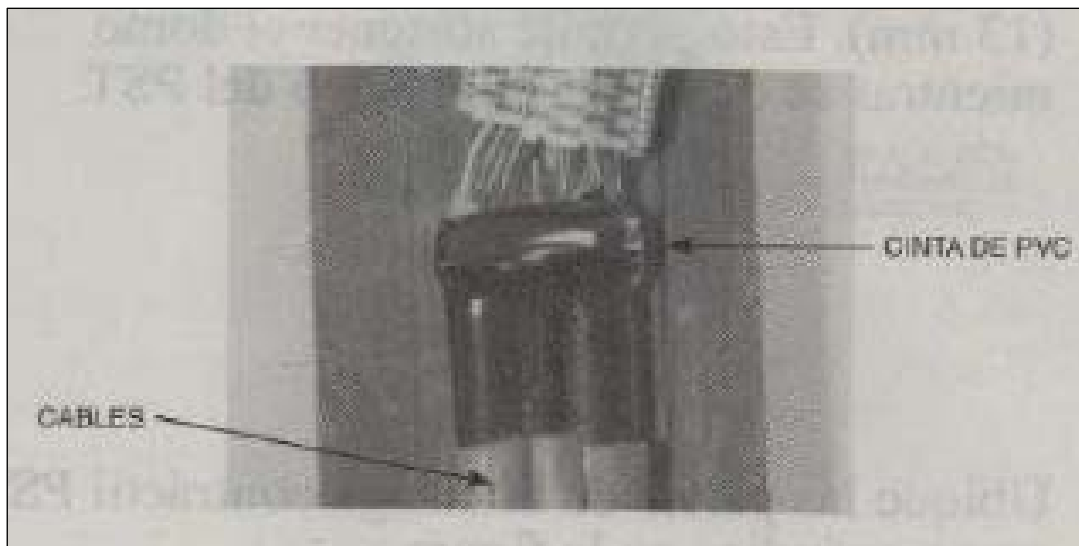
Aplicación de la Cinta de PVC Sobre los Conectores y la Malla Conductora.
